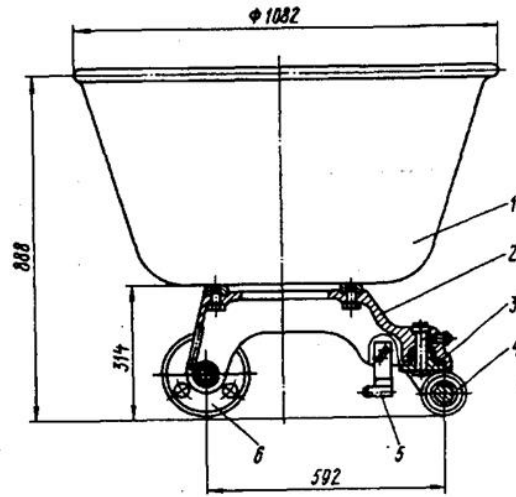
Загальний вид діжі підкатної марки Т1–ХТ2Д:
